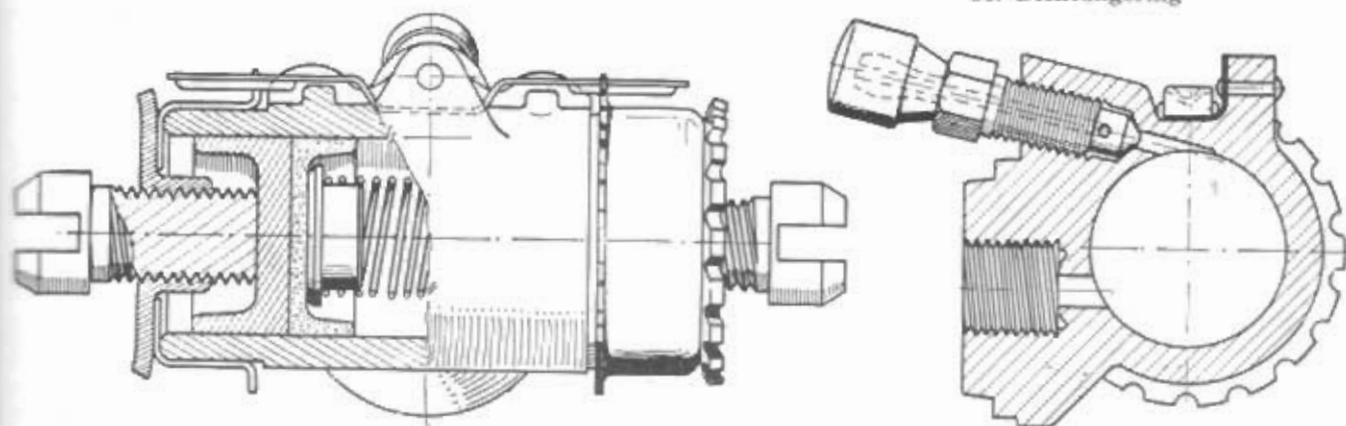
Radbremszylinder (Bremsbacken-Druckzylinder)
